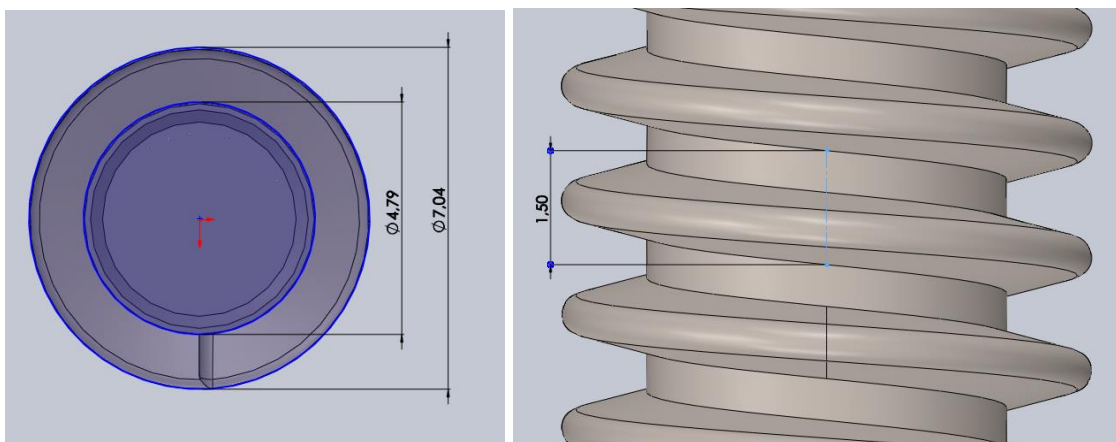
Vista superior e lateral com dimensões dos fusos autotravantes.
